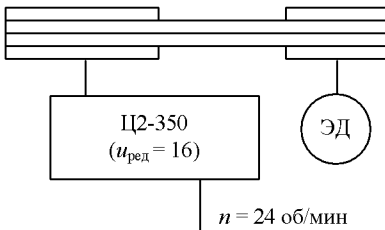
Схема привода строгально-го станка с клиноременной передачей
